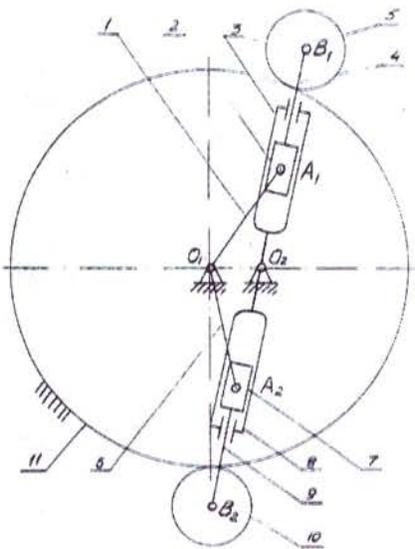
Планетарный фрикционный механизм с двойным сателлитом (шпинделей) с внешним перекачиванием колес:
